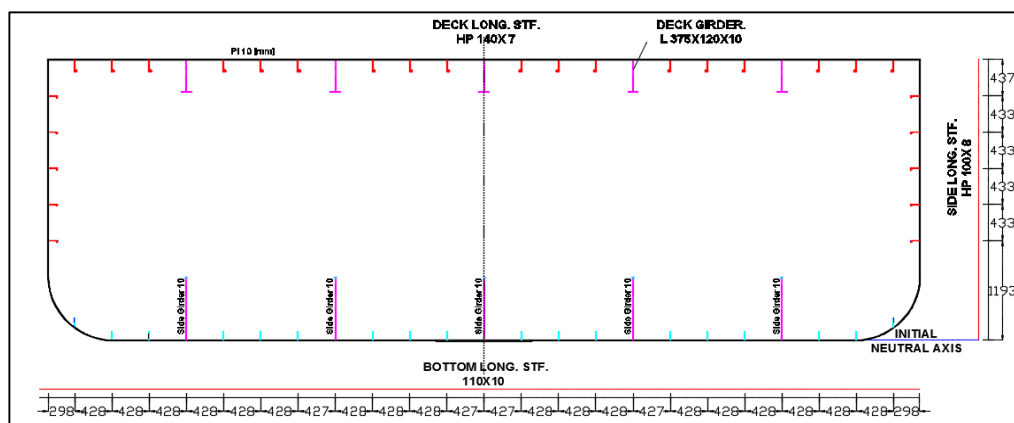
Sección considerada en el cálculo del módulo seccional.
